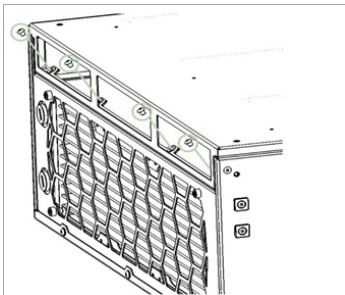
Извлечение винтов фиксации нижней задней крышки с корпусом
